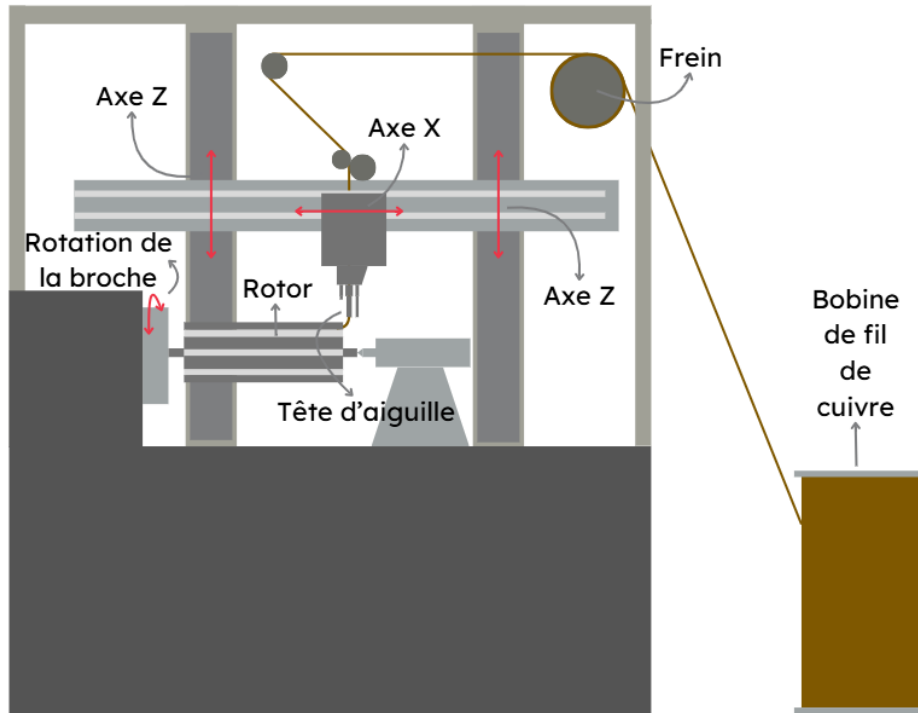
Schéma illustrant la machine pour le bobinage
